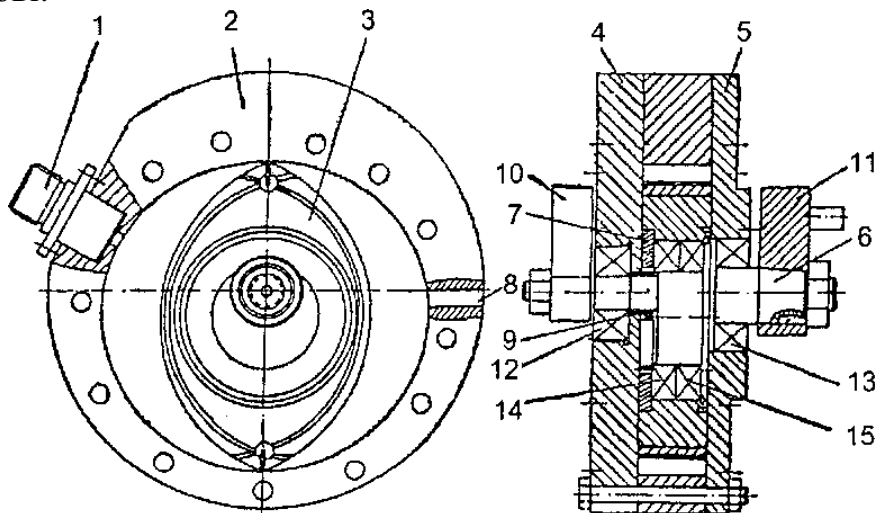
Роторно–поршневий однодуговий епітрохайдний компресор РПК–160:
